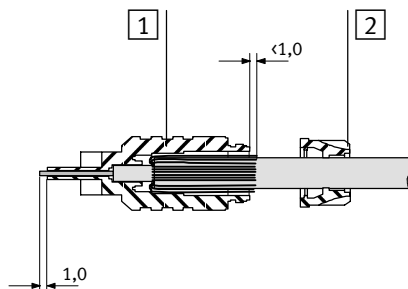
/5: Montage des Lichtwellenleiters in den IP-Link Stecker (Maßangaben in mm)
